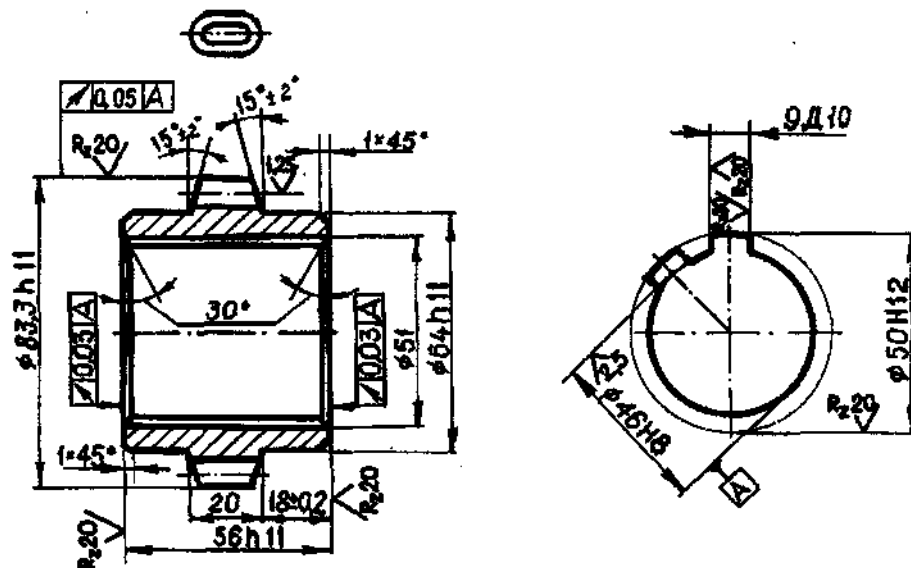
Зубчатое колесо. Деталь 6Р13.3.48ДР
